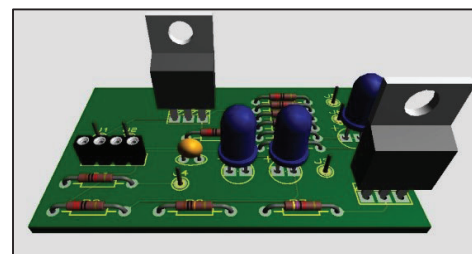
Modelado en 3D de la PCB vista superior. Fuente: Propia
